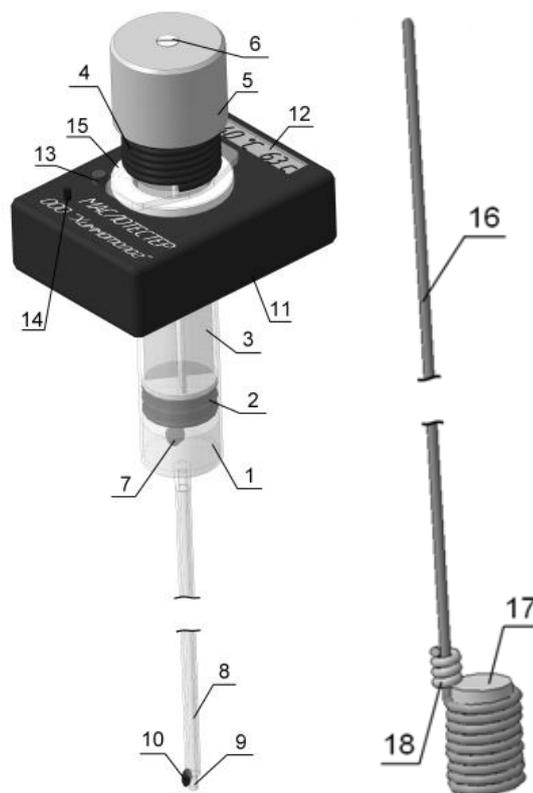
Прибор для определения вязкости смазочного материала «Маслотестер»: 1 – цилиндрическая емкость; 2 – резиновый поршень; 3 – шток; 4 – пружина; 5 – крышка; 6 – винт; 7 – поплавок; 8 – внешняя трубка; 9 – внутренняя трубка; 10 – термомпара; 11 – измерительный блок; 12 – дисплей; 13 – кнопка включения/выключения; 14 – кнопка сброса времени; 15 – шайба; 16 – шомпол; 17 – магнит; 18 – медная проволока.
